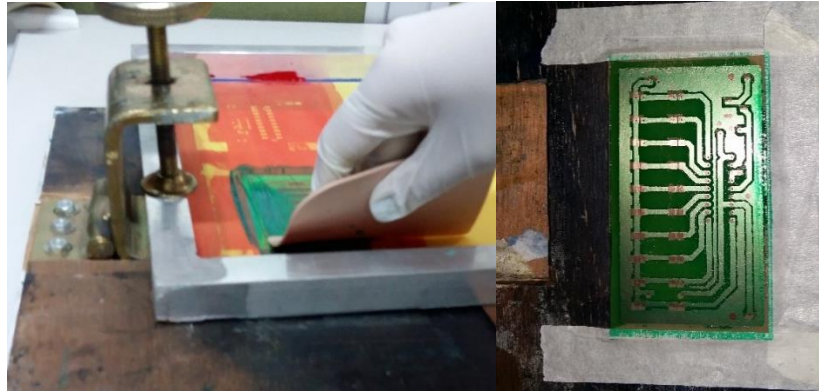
Impresión de la tinta UV y PCB con antisolder.
